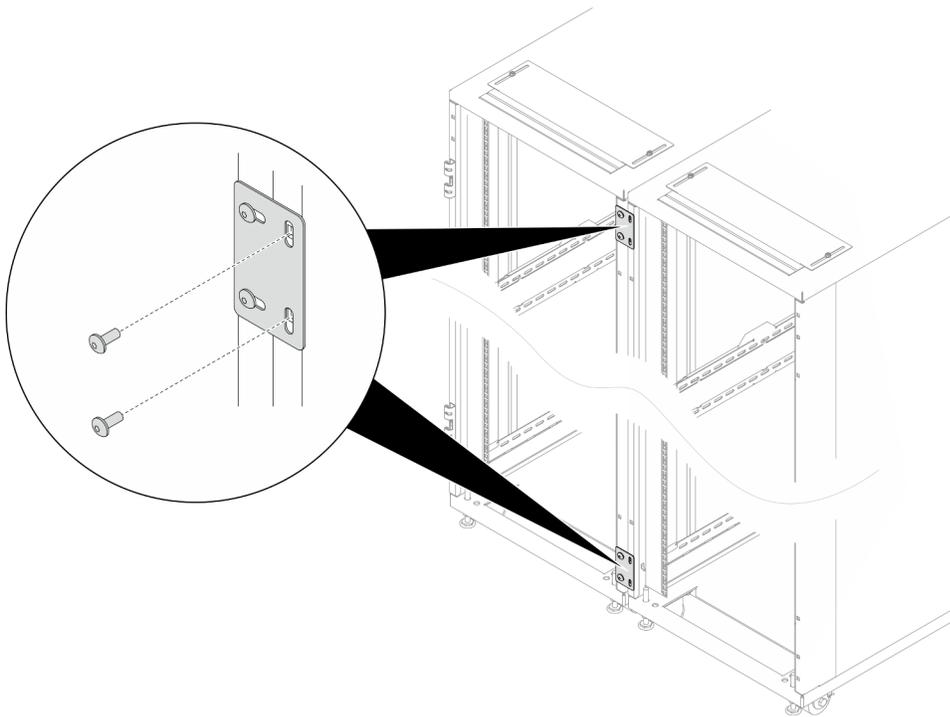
Rimozione delle viti per preparare l'installazione dell'estensione
